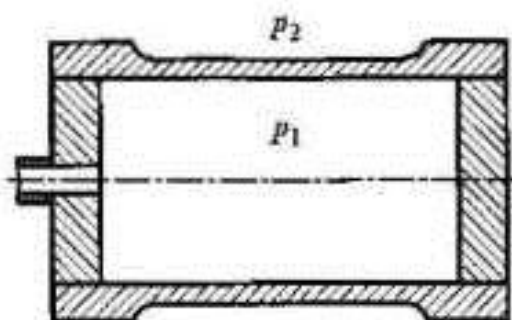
Трубчатый образец, нагруженный внутренним и внешним давлениями
